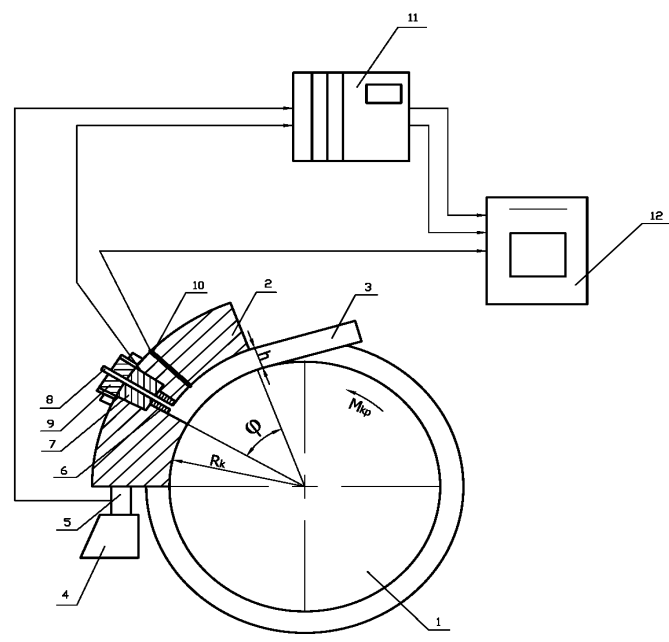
Схема измерения параметров непрерывного прессования на установке Конформ: 1 – приводное колесо с калибром, 2 – кольцевая вставка, 3 – заготовка, 4 – упор, 5 – мездоза момента, 6 – пресс-матрица, 7 – мездоза давления, 8 – пресс-изделие, 9 – упорная гайка, 10 – термопара, 11 – усилитель, 12 – осциллограф
